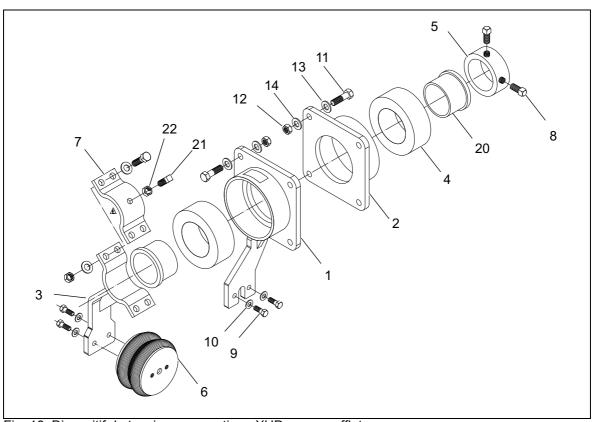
Dispositif de tension pneumatique XHD avec soufflet
